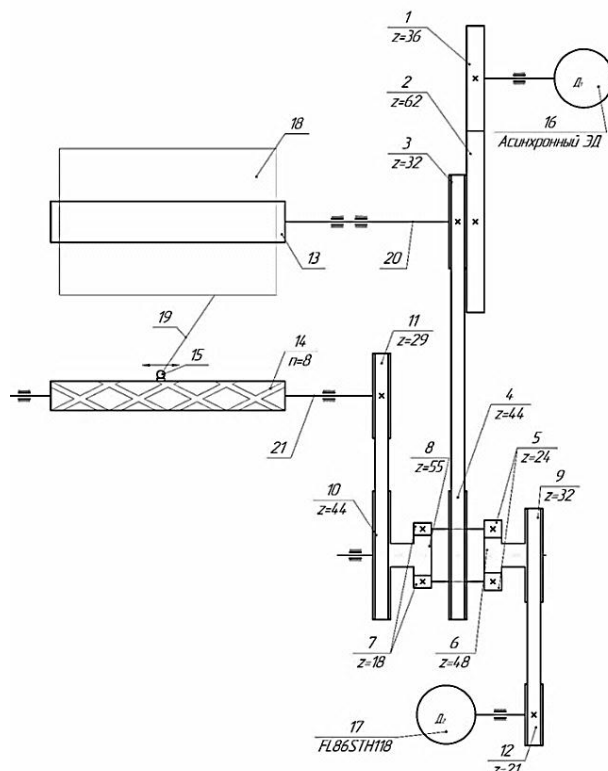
Намоточный механизм с дополнительным шаговым электродвигателем
